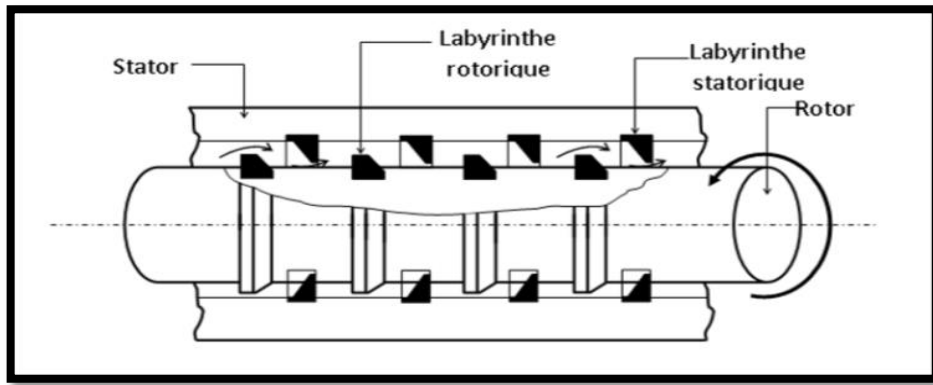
Etanchéité à labyrinthe en bout d'arbre [10]
